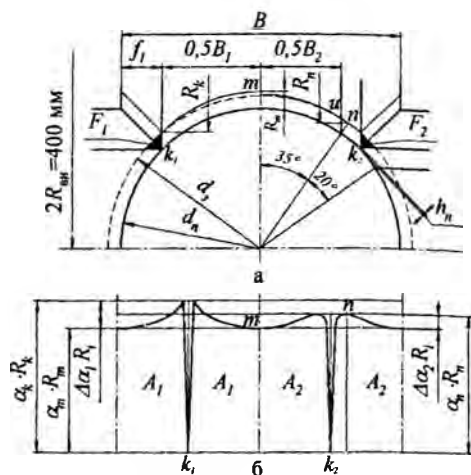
Схема калибров «круг-круг» (а) и поверхности контакта валков с заготовкой (б) в четырехвалковом калибре
